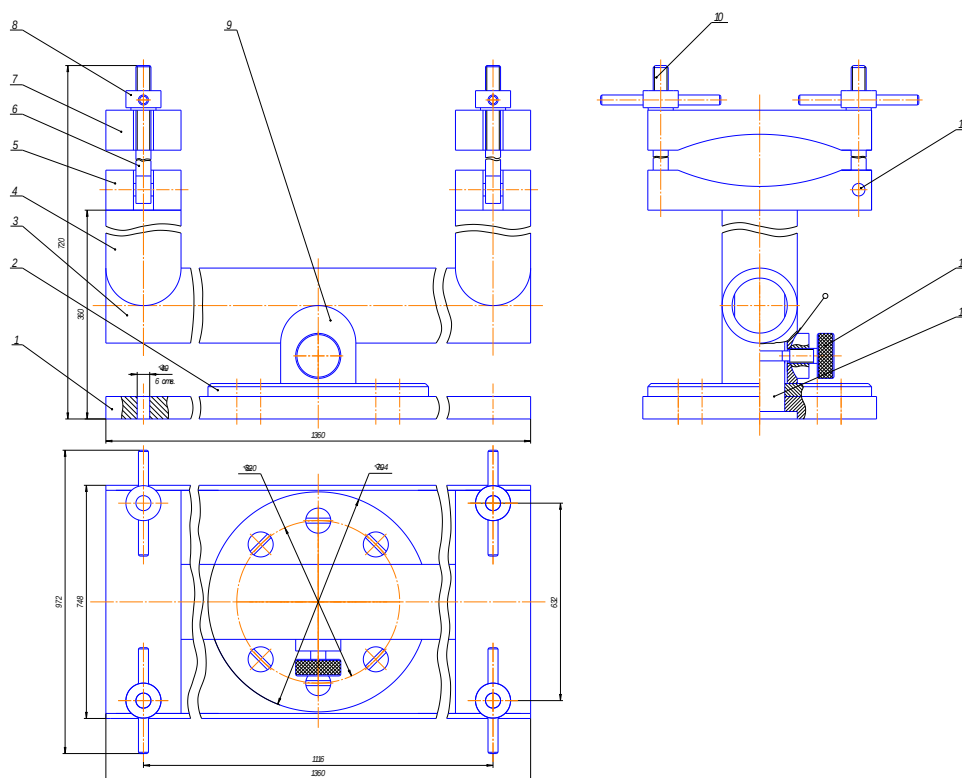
Приспособление для разборки и сборки ведущих мостов автомобилей.
